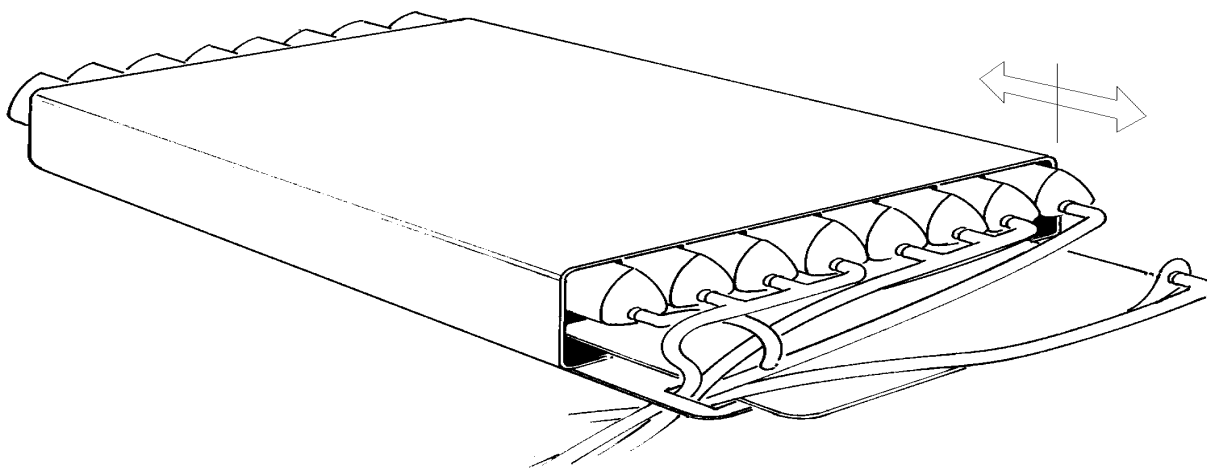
DESASSEMBLAGE / ASSEMBLAGE DU MATELAS
